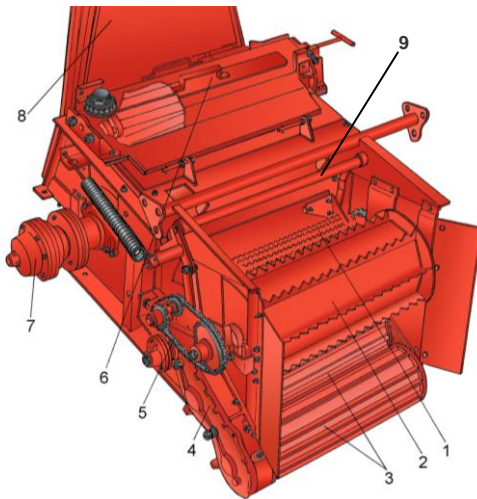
Питающий аппарат комбайна КСК-600: 1 – задний подпрессовывающий валец; 2 – передний подпрессовывающий валец; 3 – нижние передний и средний вальцы; 4 – зубчатый цилиндрический редуктор; 5 – цепная передача; 6 – задвижка; 7 – обгонная муфта; 8 – основание силосопровода; 9 – торсионный вал
